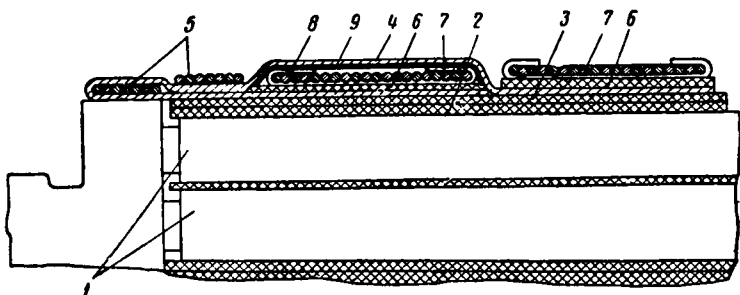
Разрез передней лобовой части обмотки якоря тягового двигателя ДК-103А:
